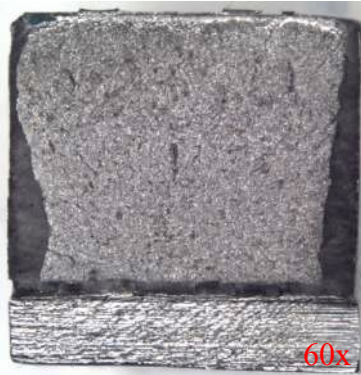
Vista macroscópica de la fractura 22MnB5, -36°C, condición 2.
